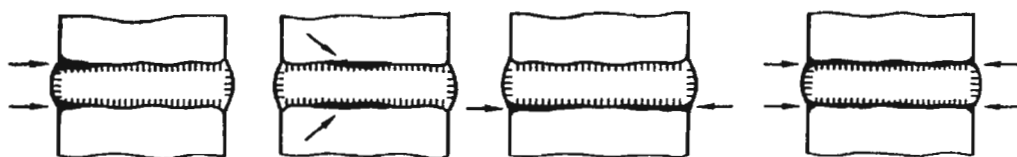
Непровары в электрошлаковых сварных соединениях
